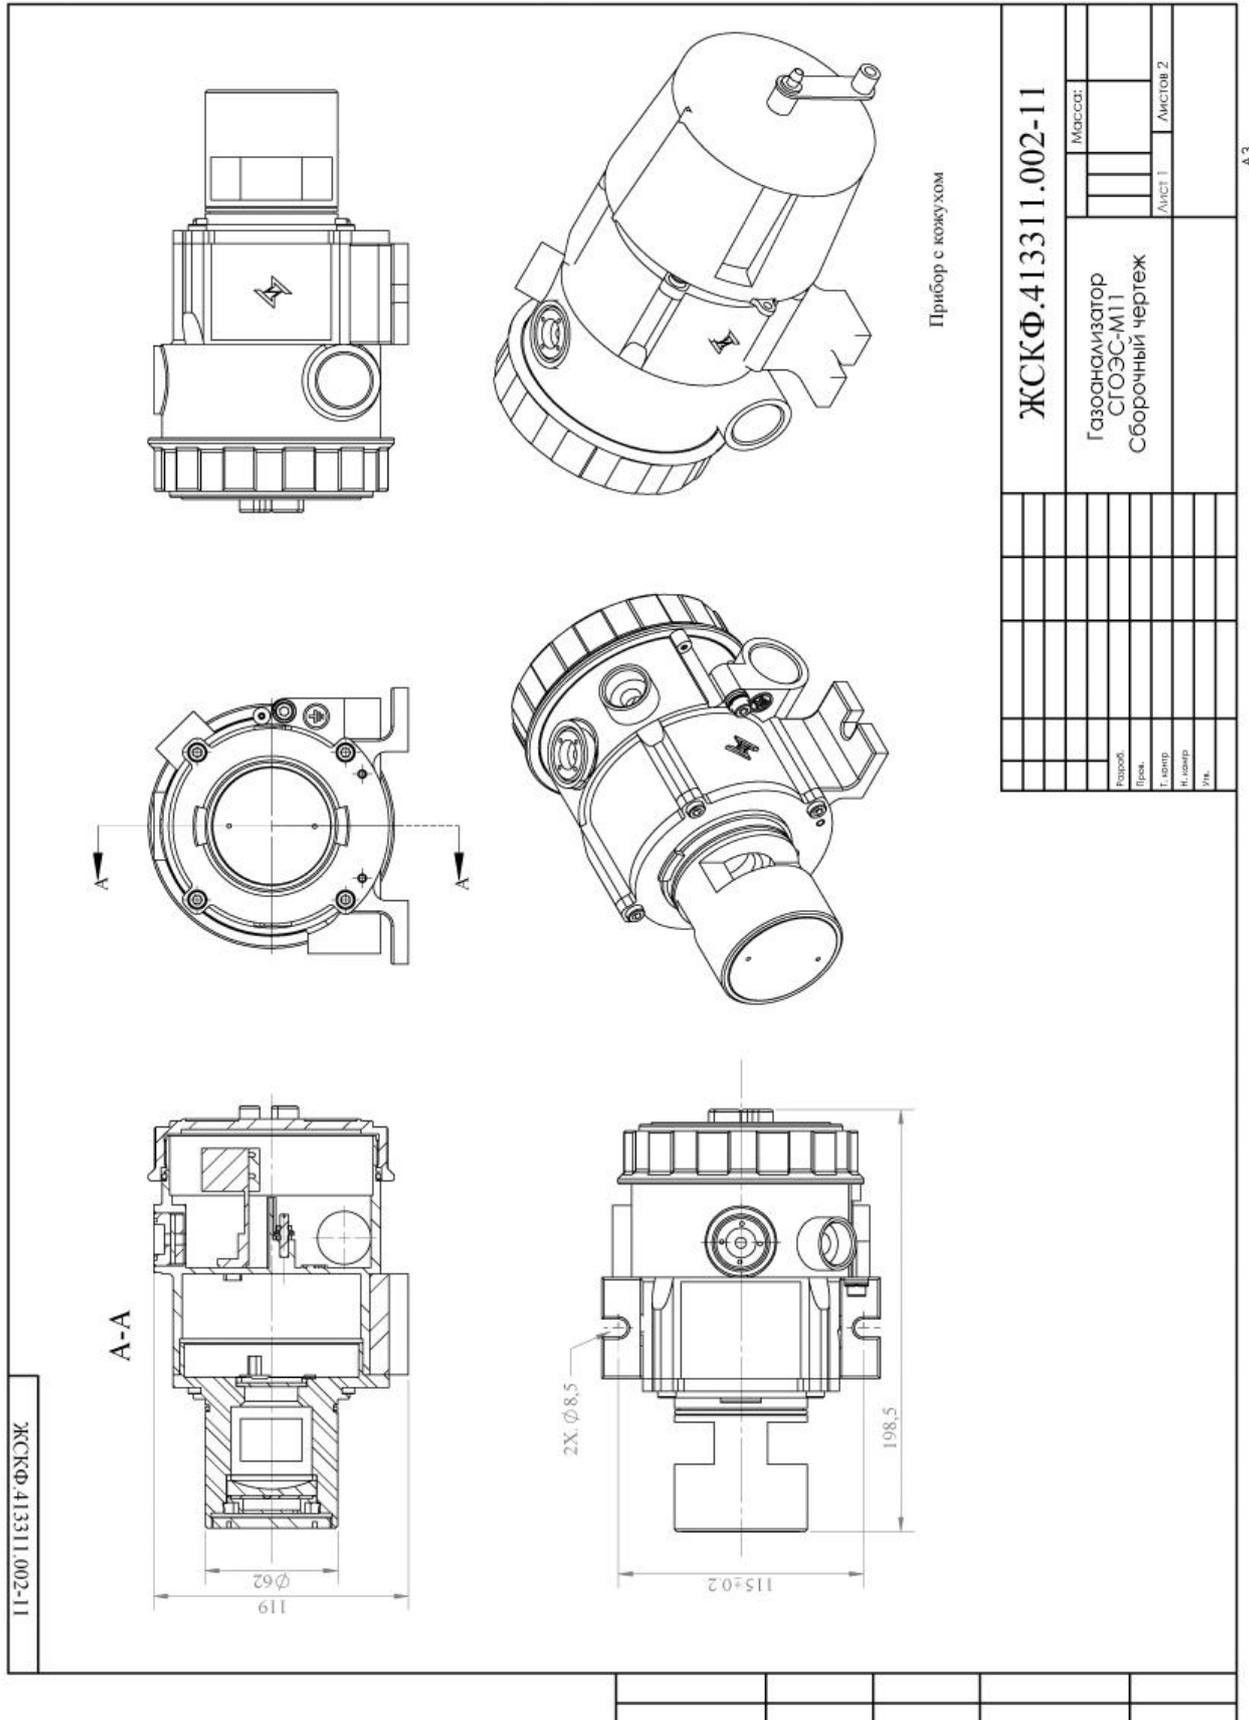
Сборочный чертеж газоанализатора СГОЭС
